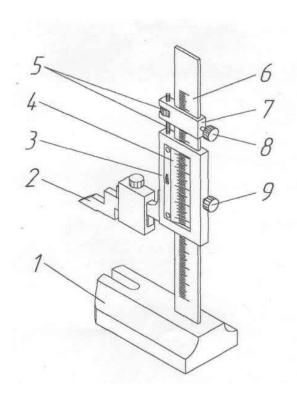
Штангенрейсмас для разметки заготовок: 1— основание; 2 — разметочная ножка; 3 — рамка; 4 — нониус; 5 — винт и гайка микрометрической подачи; 6 — штанга; 7 — рамка микрометрической подачи; 8 — зажим рамки микрометрической подачи; 9 — зажим рамки
